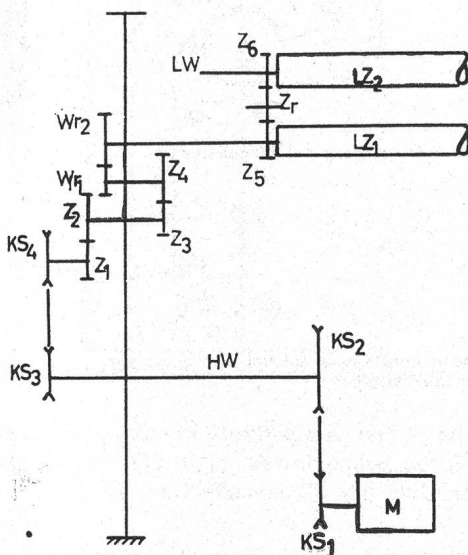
Schemaskizze zum Antrieb der Lieferzylinder
